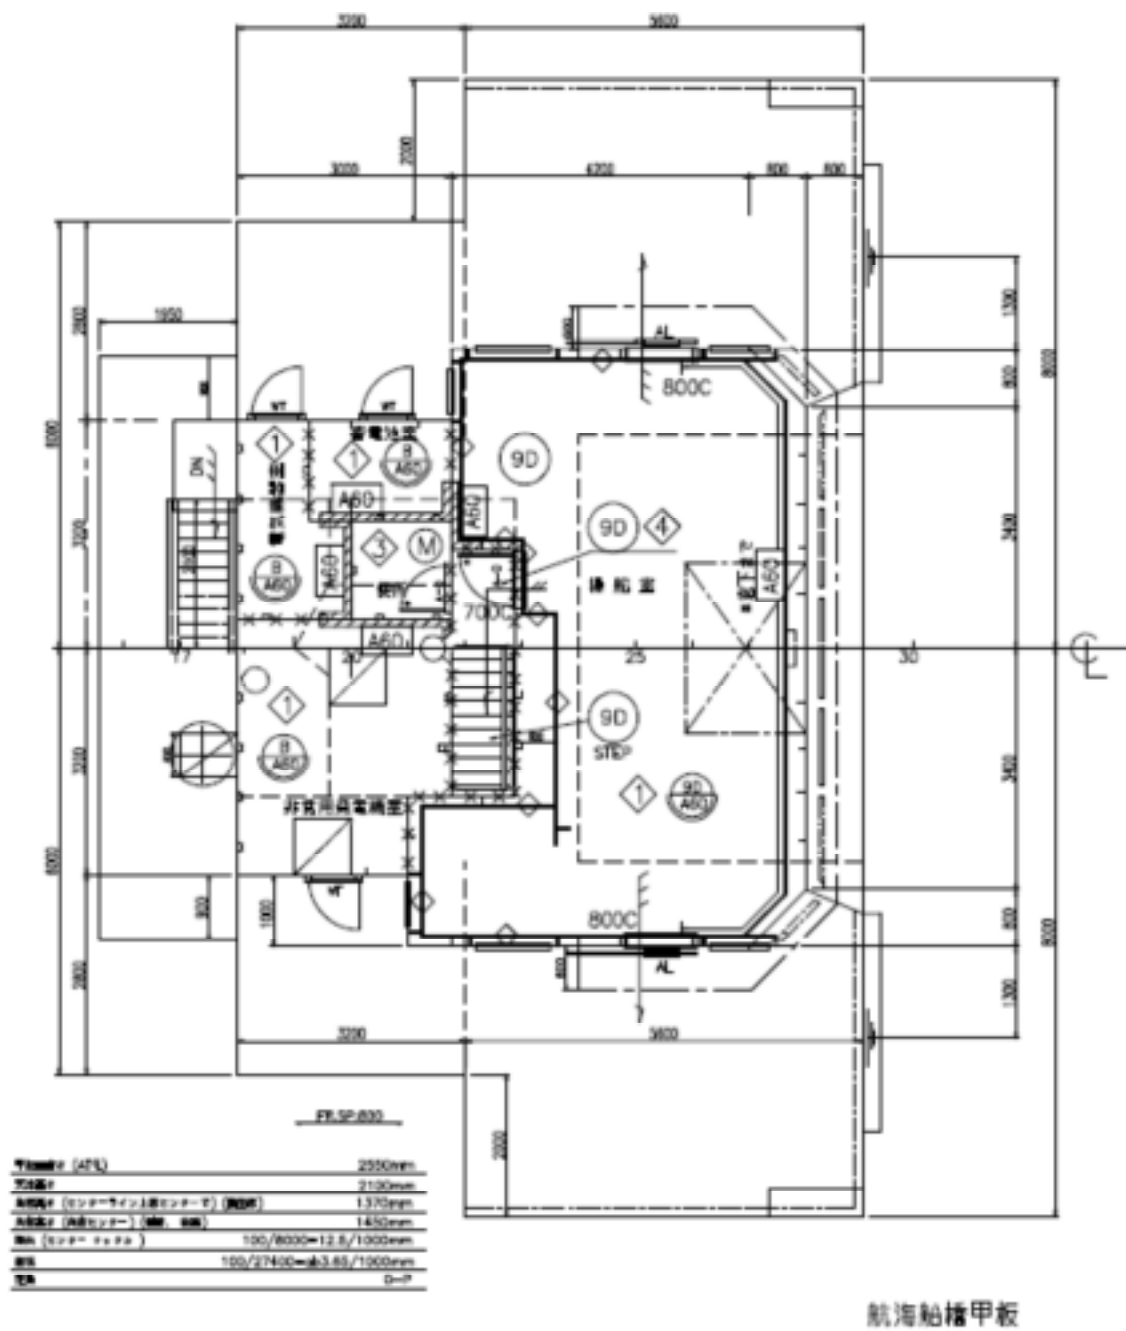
(1) 居室内装仕様 (Nav. Bri. Deck)
